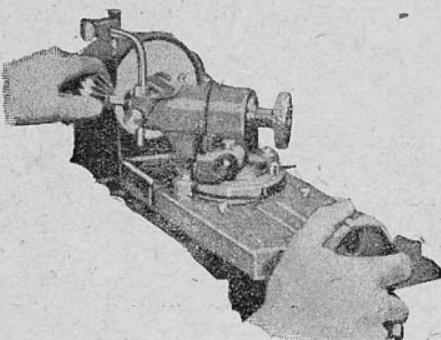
Установка щарошки в патрон, монтированный на салазках станка
